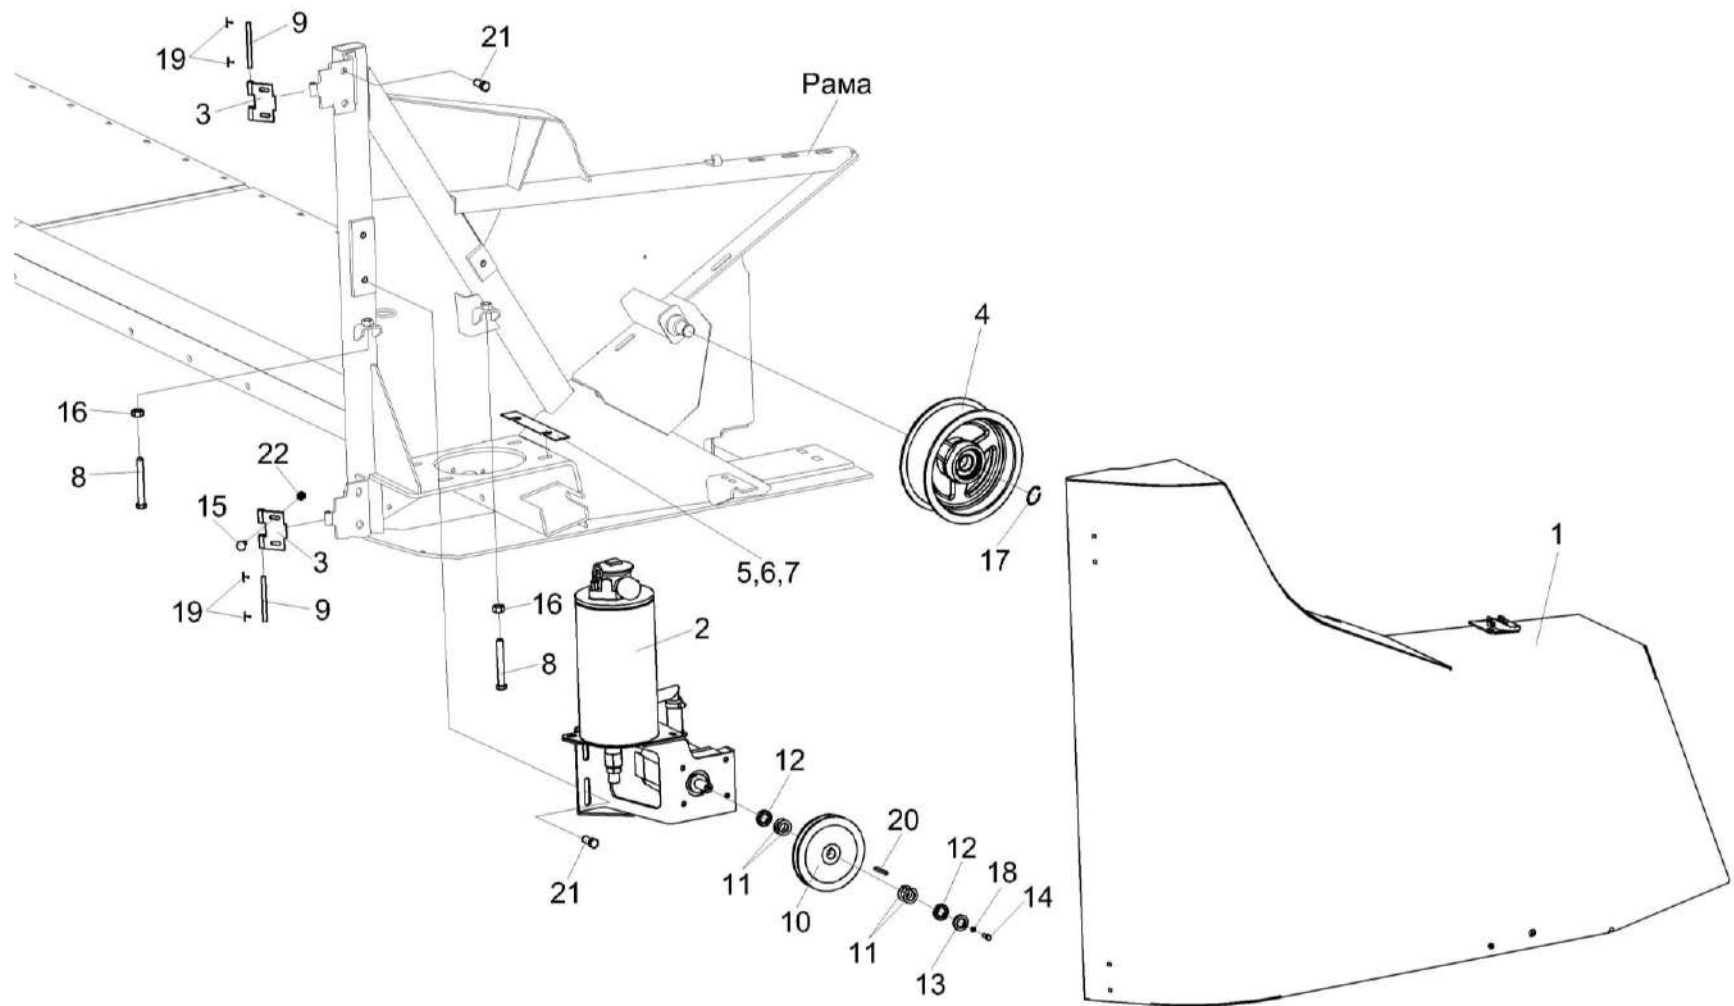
Приспособление для уборки рапса КЗК-9-1-1540000 (лист 3)
